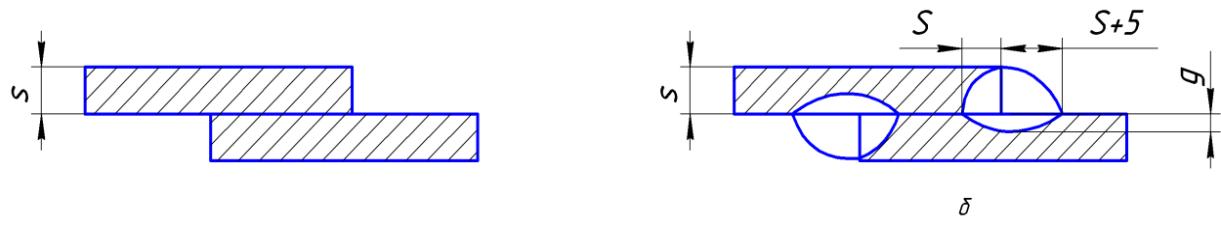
Сварное соединение до (а) и после сварки (б)
